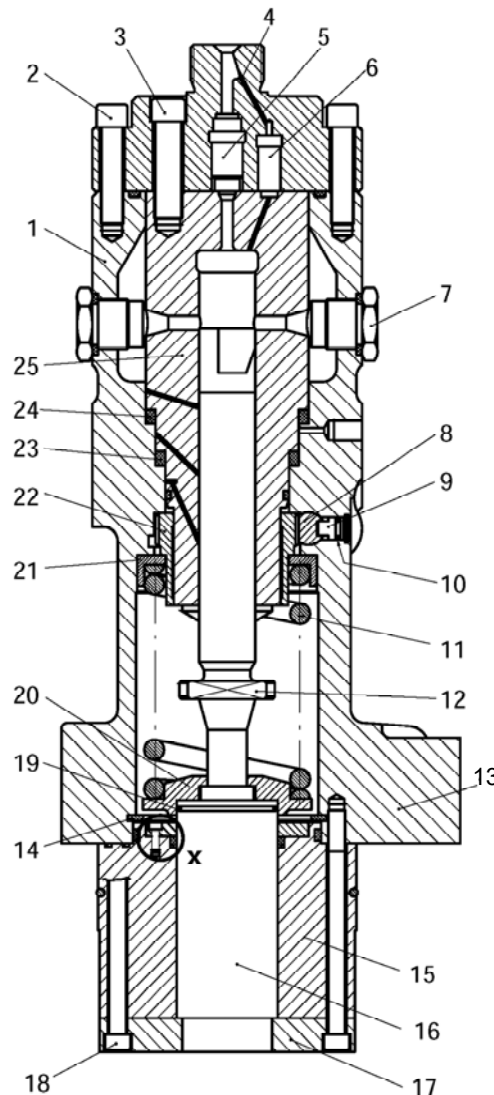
ПНВТ дизеля М 32С: 1 – корпус; 2, 3, 18 – болти кріплення; 4 – байпасний канал; 5 – зворотний клапан; 6 – байпасная порожнина; 7 – контрольні пробки з дифузійним компенсатором; 8 – зубчастий сектор; 9 – рейка; 10 – напрямна; 11 – зворотна пружина; 12 – плунжер; 13 – привалочний фланець; 14 – ущільнення; 15 – напрямна; 16 – упор; 17 – фланець; 19 – регулювальна шайба; 20 – нижня тарілка; 21 – верхня тарілка; 22, 23, 24 – ущільнення
